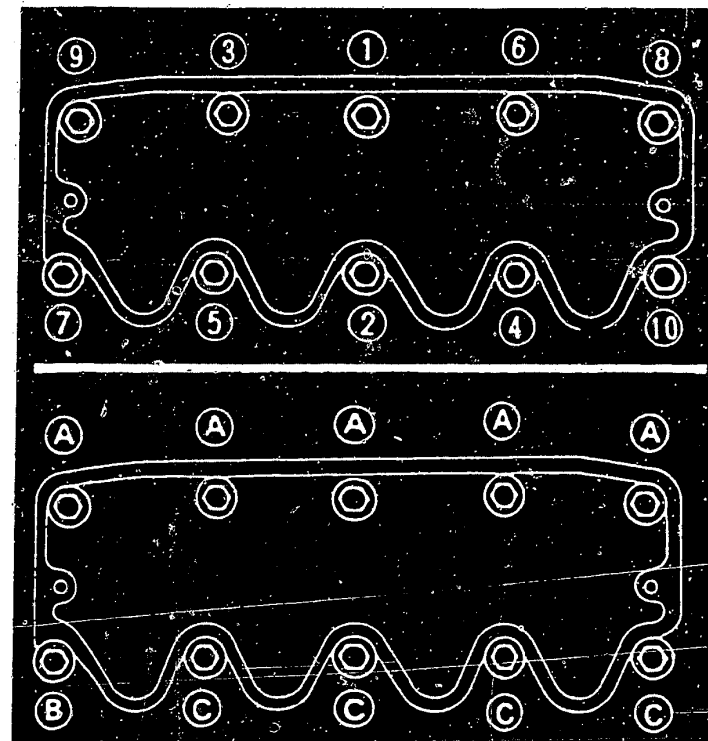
Oben: Anzugsreihenfolge der Zylinderkopfschrauben. Unten: Die unterschiedlich langen (L) Zylinderkopfschrauben sind mit verschiedenen Drehwinkeln (letzter Schritt) anzuziehen. A) L = 95mm, Anzug = 45...50° - B) L = 110mm, Anzug = 55...60° - C) L = 80mm, Anzug = 40...45°.
